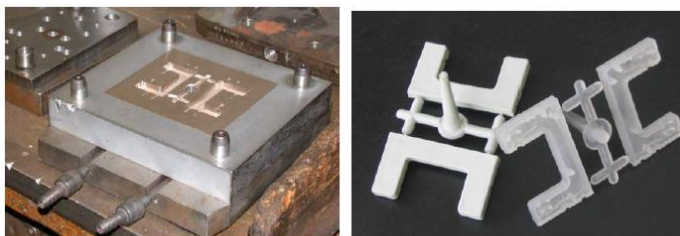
Вставка для ТПА и отливки ABS-пластика
